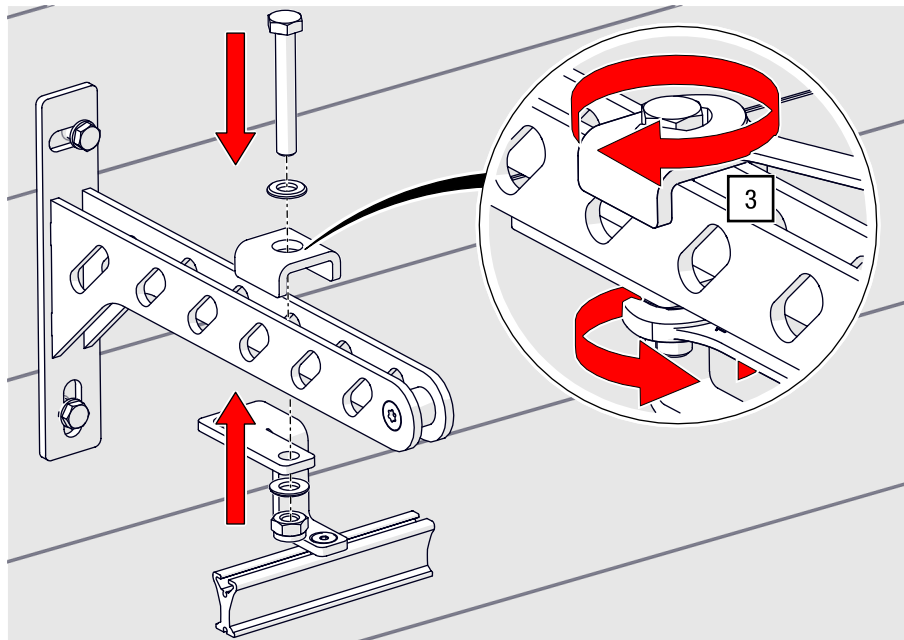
Wandarm mit Abhängung für Seilführung verschrauben
